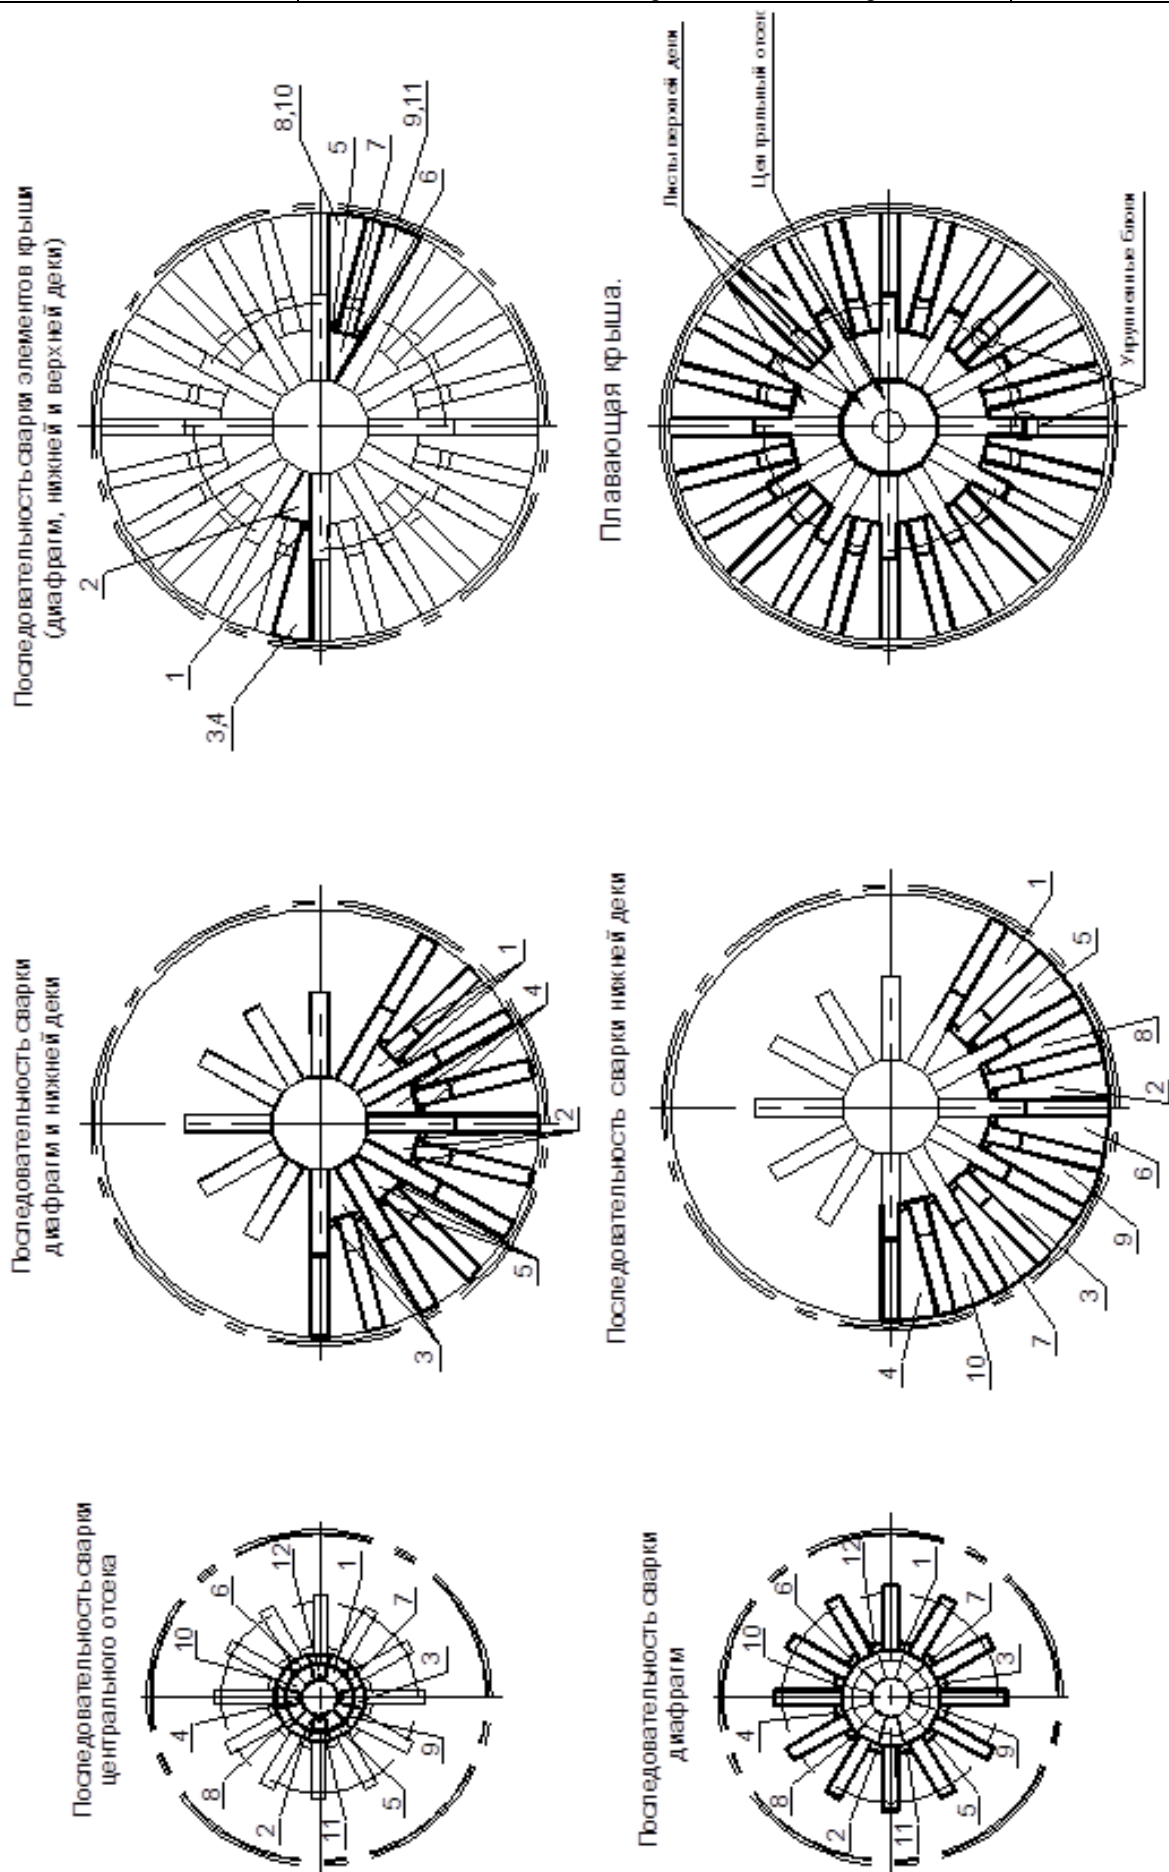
Последовательность сборки и сварки двудечной плавающей крыши
